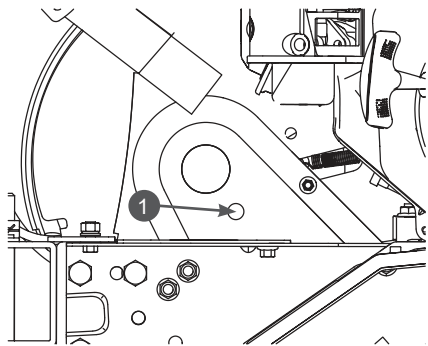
Расположение пробки отверстия для добавления смазки в редуктор
